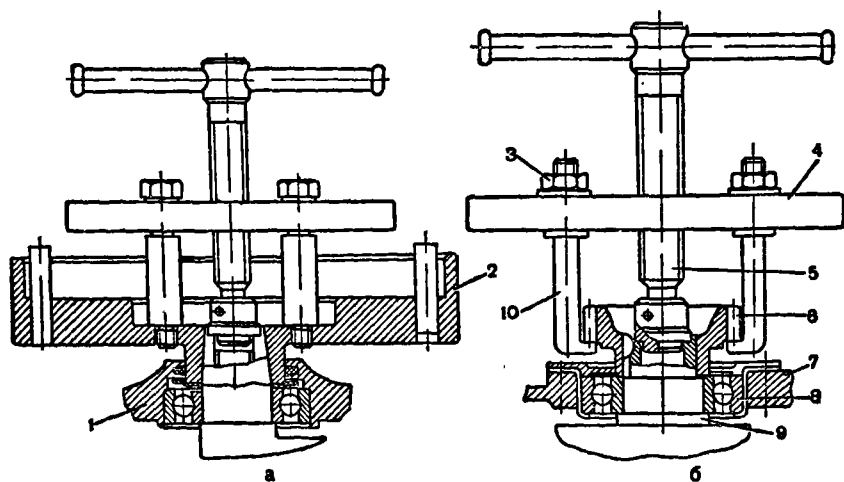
Снятие маховика (а) и ведущего зубчатого колеса (б):
